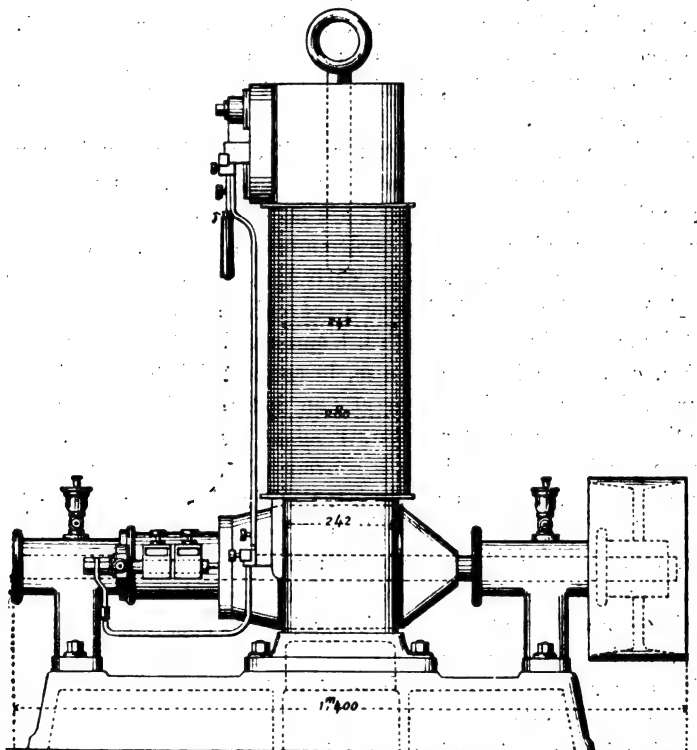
Machine Edison-Hopkinson. — Vue latérale.
